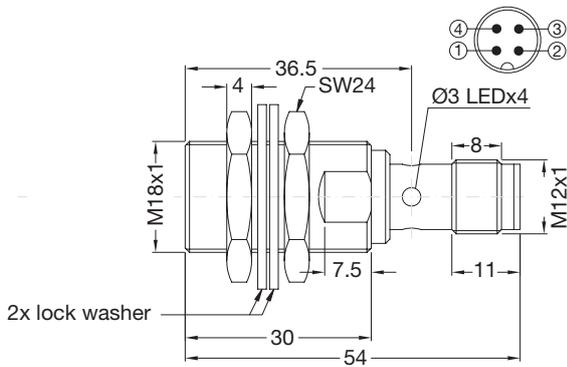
Kurze Ausführung, bündiger Einbau, Steckversion
